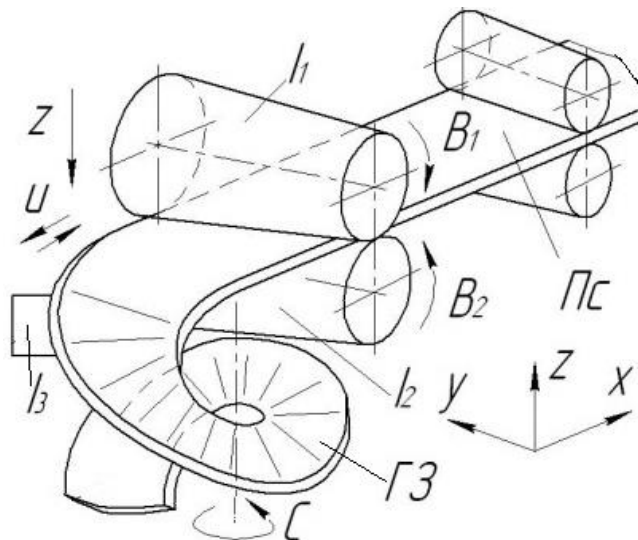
Виготовлення гвинтової заготовки способом асиметричного обтискання смугової заготовки: $ГЗ$ – гвинтова заготовка, $Пс$ – смугова заготовка, I_1 , I_2 , I_3 – відповідно прокатні валки та клин для відгинання $ГЗ$.
